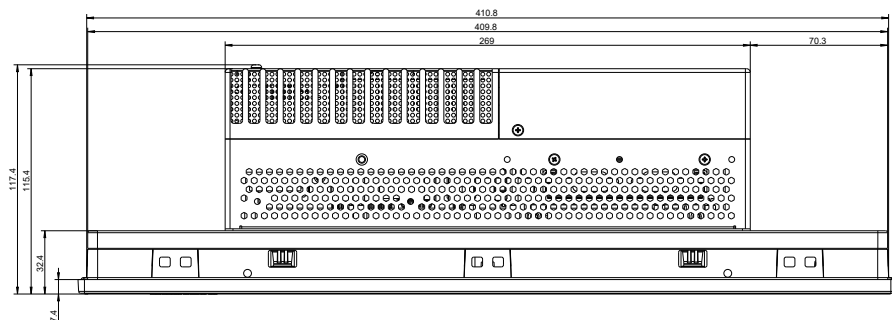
Размеры корпуса устройства VR4x15, вид сверху
